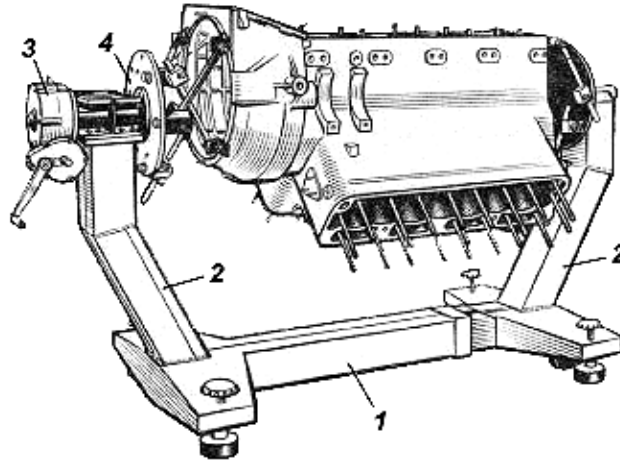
Стенд для розбирання двигунів [5]
